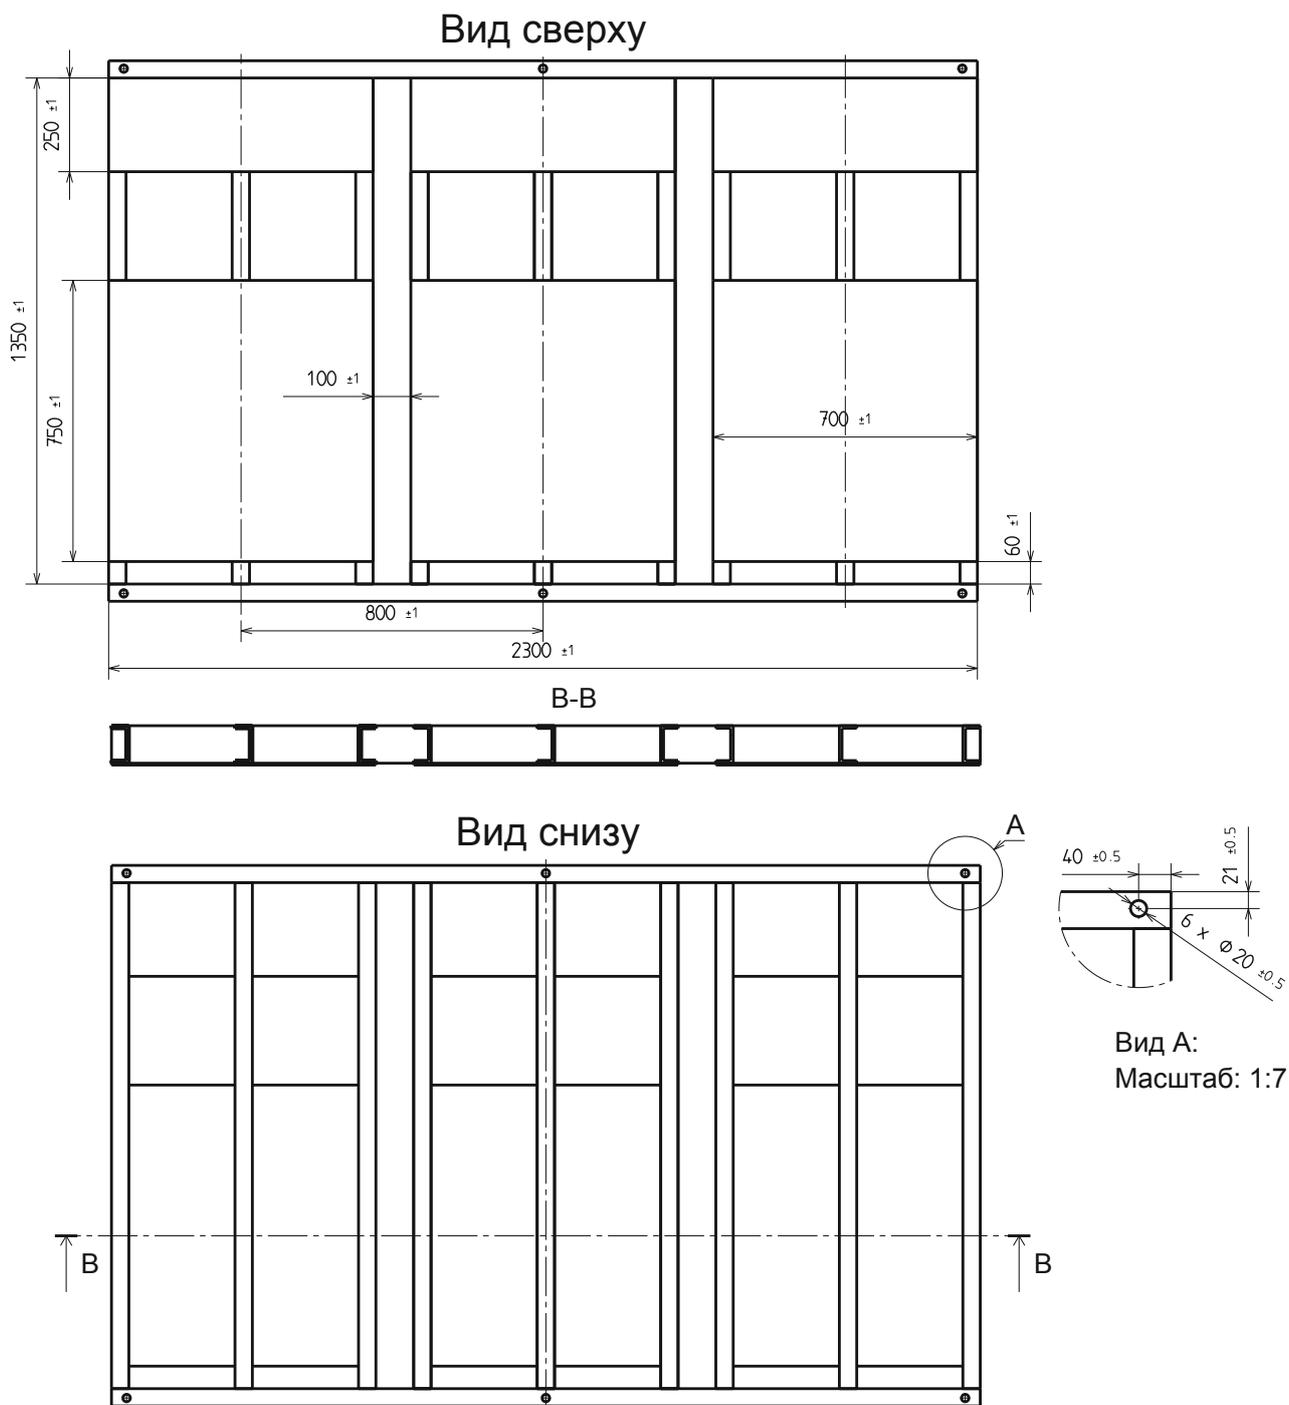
Рама-основание для установок пожаротушения Hydro MX 2/1 на насосах NB.
